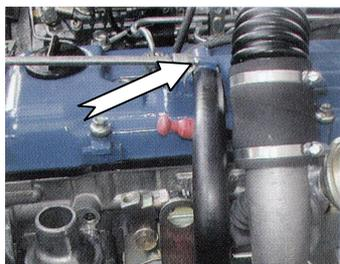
Крепление трубки пневмокамеры механизма регулирования.
